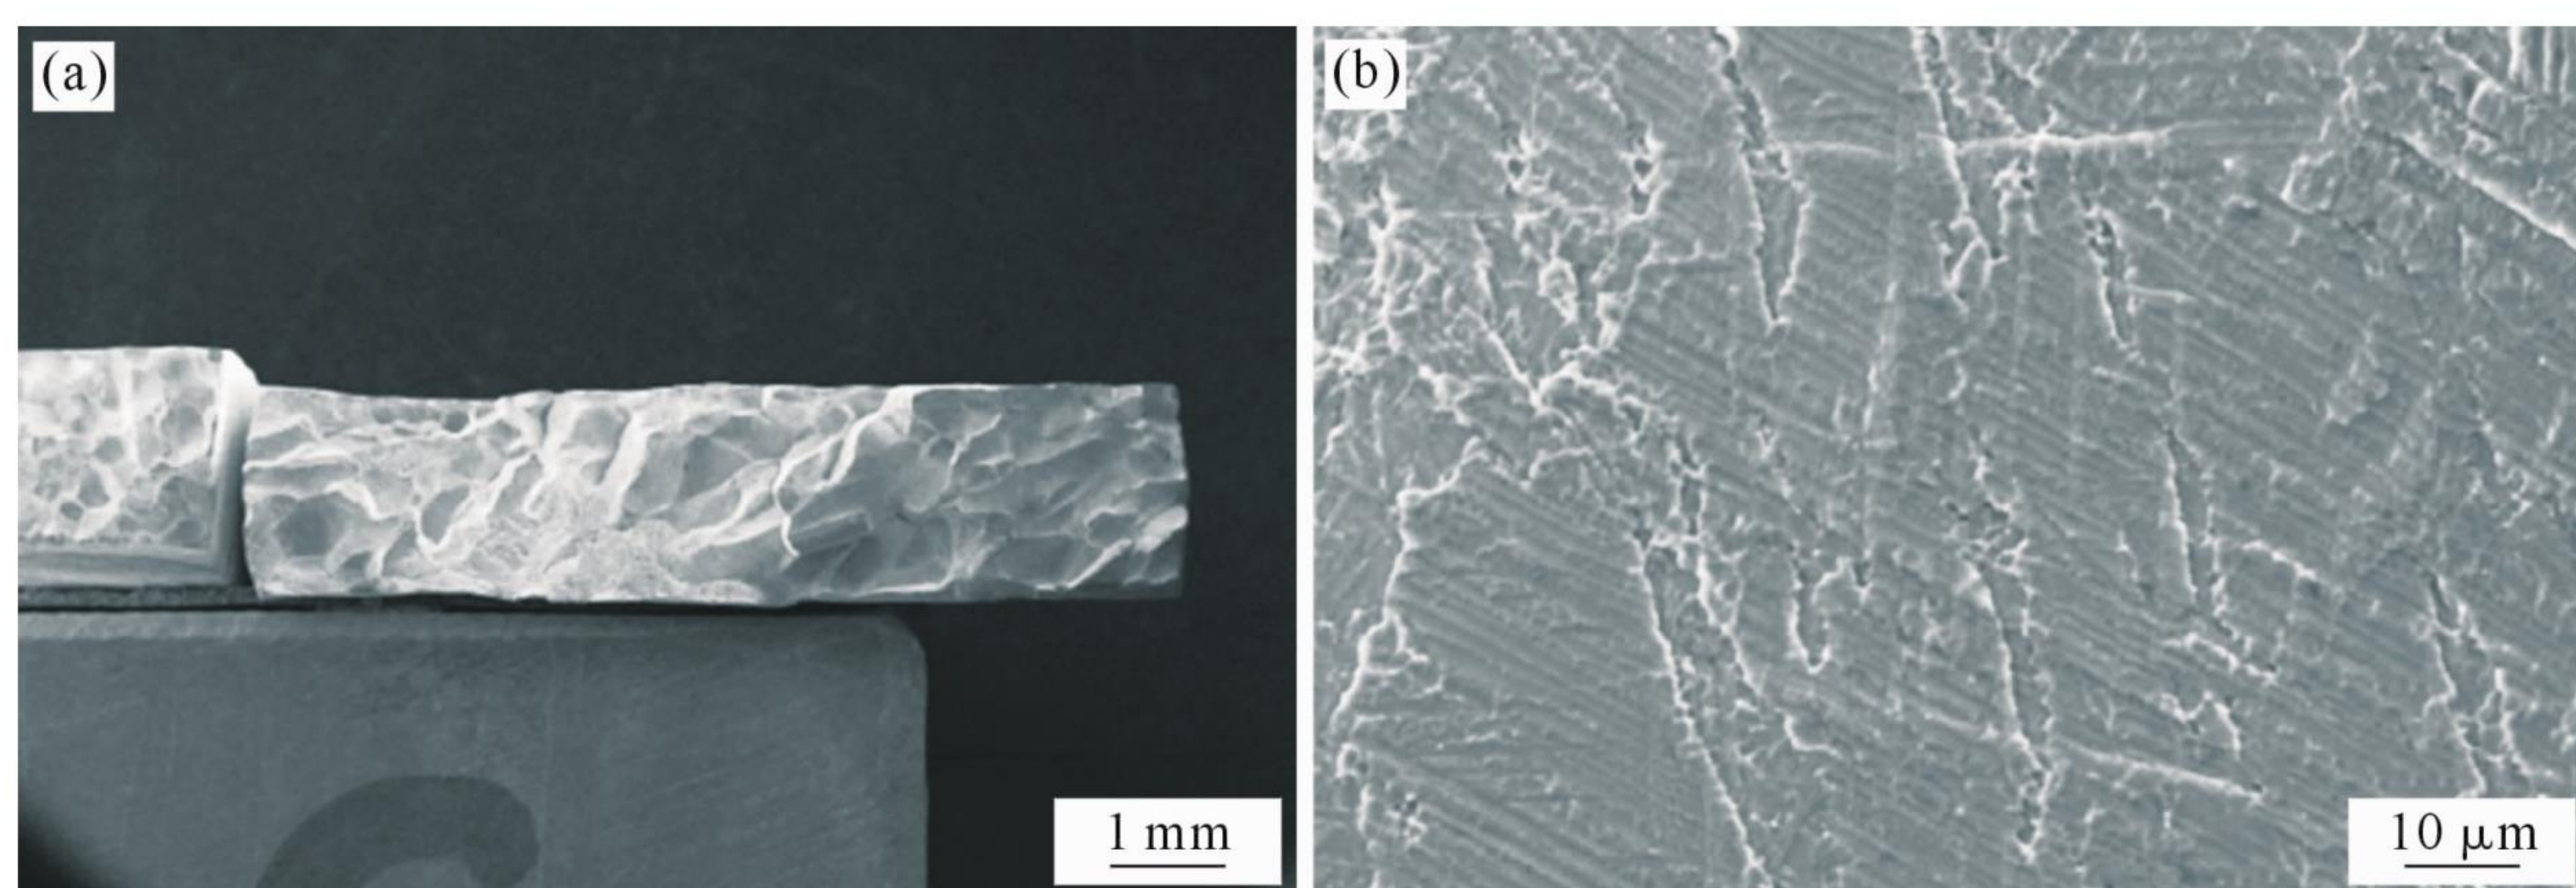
A15粉末-锻件焊接接头高温持久断口形貌:(a)宏观形貌;(b)微观形貌
